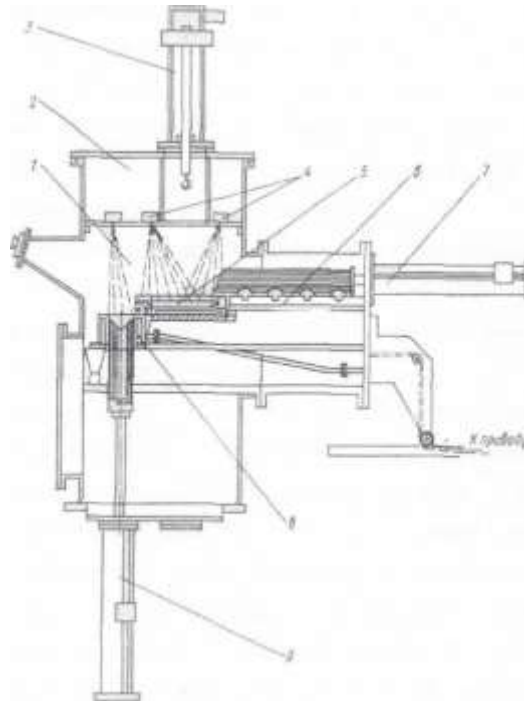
Схема електронно–променевої установки: 1 – камера плавки; 2 камера ЕПП; 3–механізм вертикальної подачі заготовки; 4– електронно–променева гармата; 5–проміжна ємність; 6–заготовка; 7– механізм горизонтальної подачі заготовки; 8–кристалізатор; 9–механізм витягування зливка
